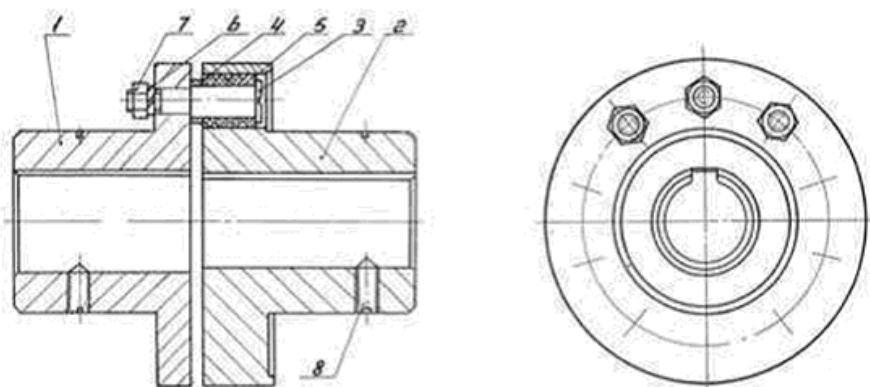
Внешний вид муфты упругой втулочно-пальцевой: 1, 2 – полумуфты; 3 - палец; 4 – втулка распорная; 5 – втулка упругая (допускается выполнять набор колец); 6 – шайба (гровер); 7 – гайка; 8 – установочный винт
